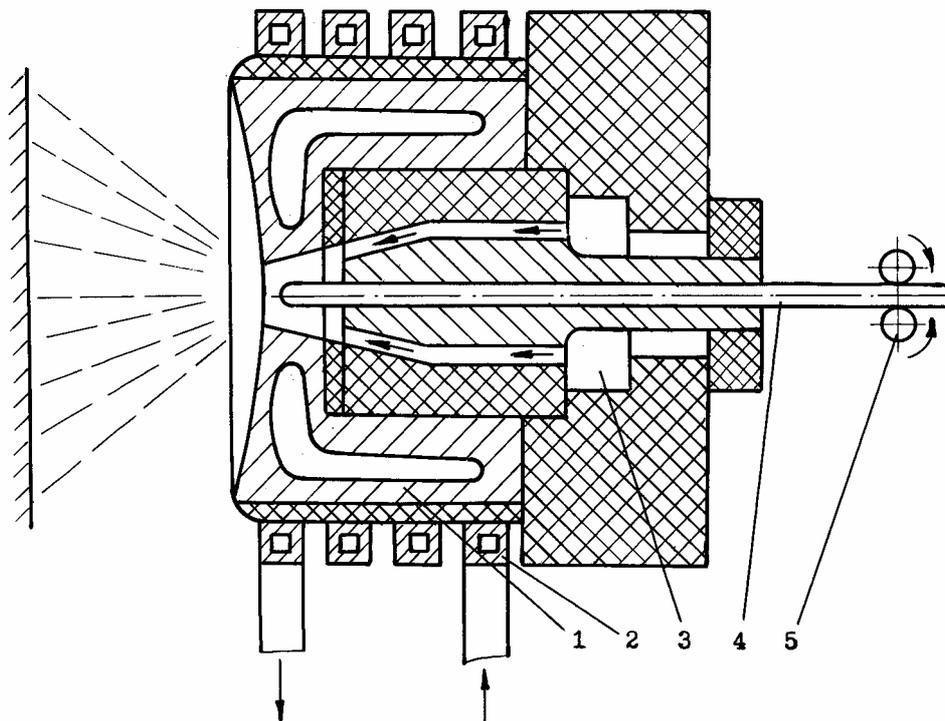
Устройство для индукционного напыления: 1 – концентратор тока; 2 – индуктор; 3 – канал воздушный; 4 – проволока; 5 – ролики подающие
